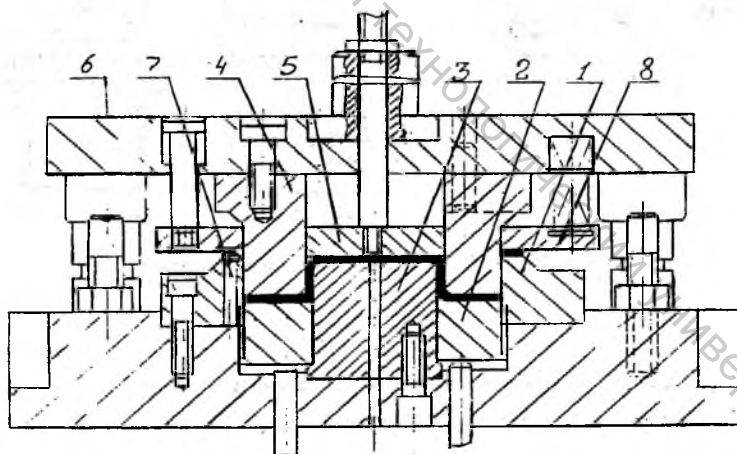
Комбинированный штамп для одновременной вырубки и вытяжки
